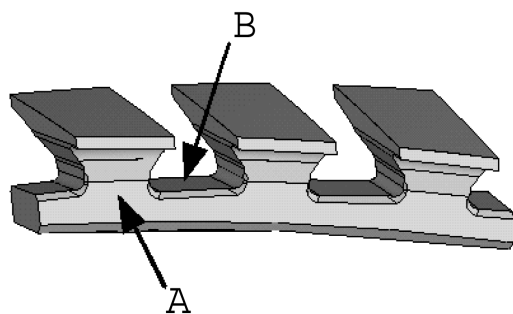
Фрагмент ободной части диска компрессора высокого давления с пазами типа "ласточкин хвост": А – боковая поверхность ножки межпазового выступа, В – доньшко паза.
